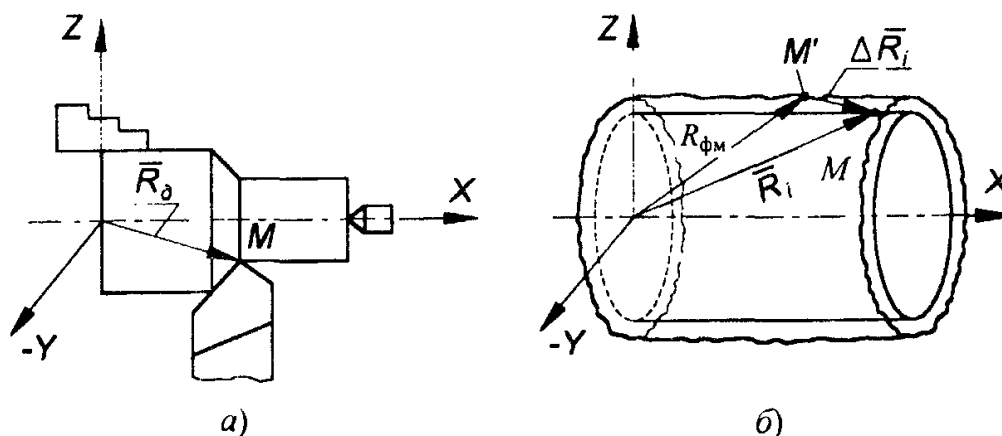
Схеми для токарної обробки заготовки (а) та формування похибки обробки \bar{R}_i в точці М деталі (б).
